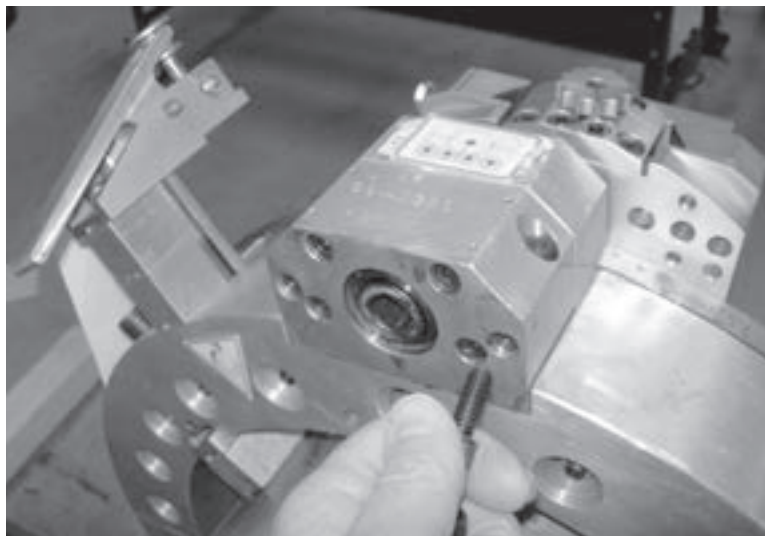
Quite los tornillos de montaje del motor de la caja del piñón y guárdelos en un lugar seguro.
